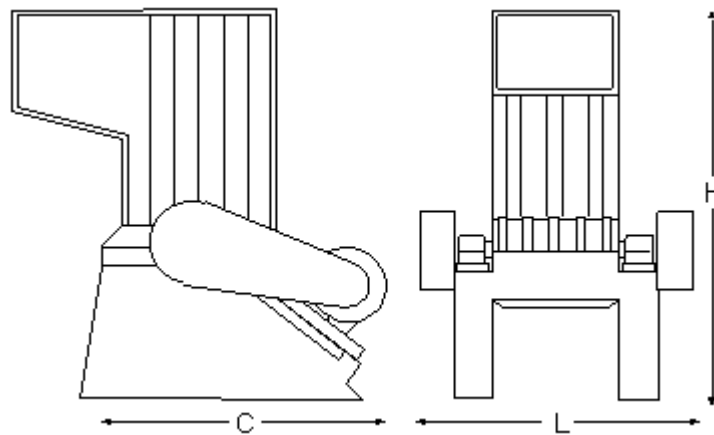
Moinho - Linha R: Desenho Dimensional, C = 1000, L = 850, H = 1300 em mm.
